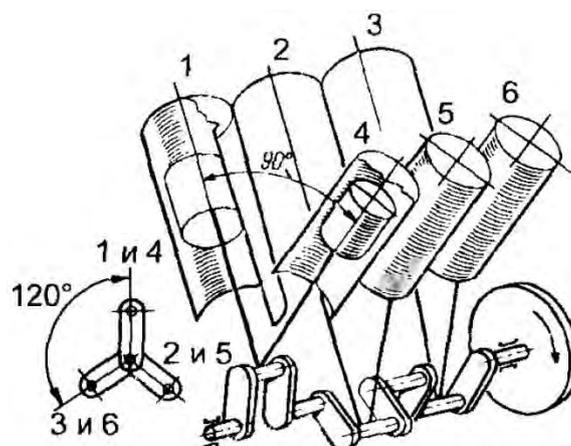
Коленчатый вал V-образного шестицилиндрового двигателя
